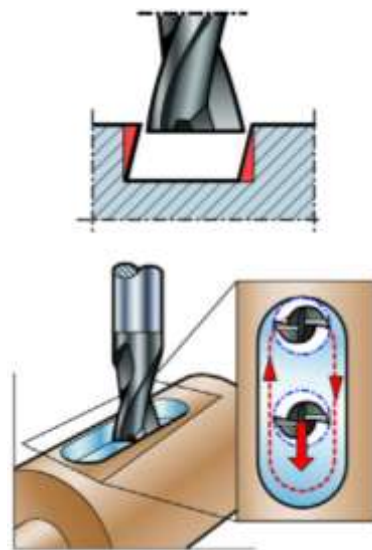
Схема обробки шпонкового паза за два проходи
